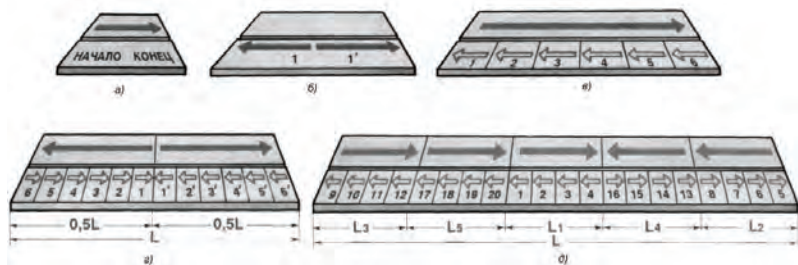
Технологии нанесения сварочного шва:
